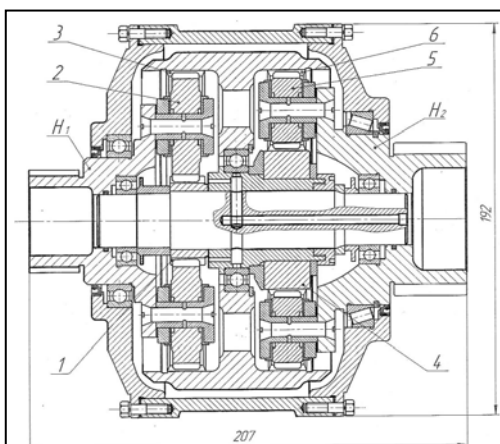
Зубчатая бесступенчато регулируемая передача. Сборочный чертеж
